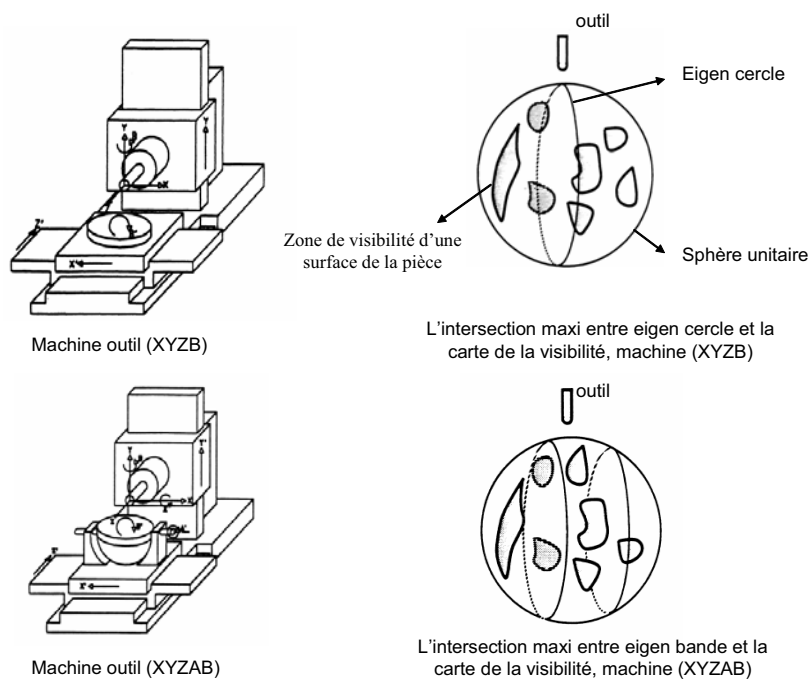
Posage de la pièce sur une machine outil à 4 et 5 axes
